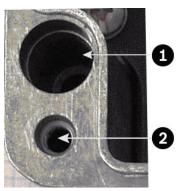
Schraubenlöcher für Gehäusemontage und Gehäusedeckel
